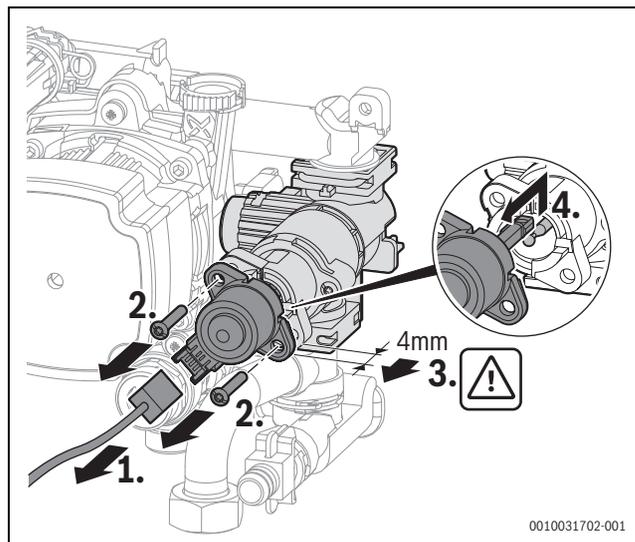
Smontare il motore sulla valvola a 3 vie (variante con viti)
